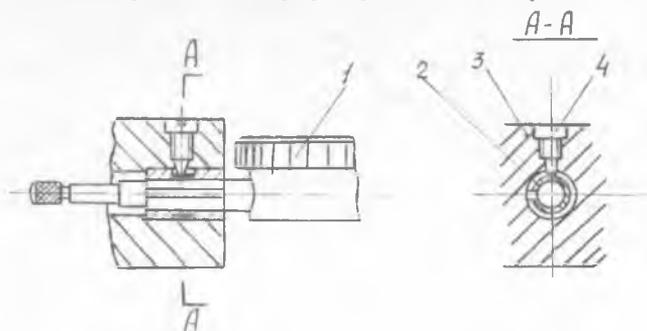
Крепление индикатора: 1 — индикатор; 2 — втулка разрезная; 3 — приспособление; 4 — винт
